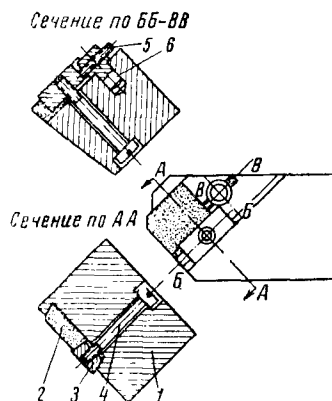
Твёрдосплавный резец-кубик с положительными передними углами
